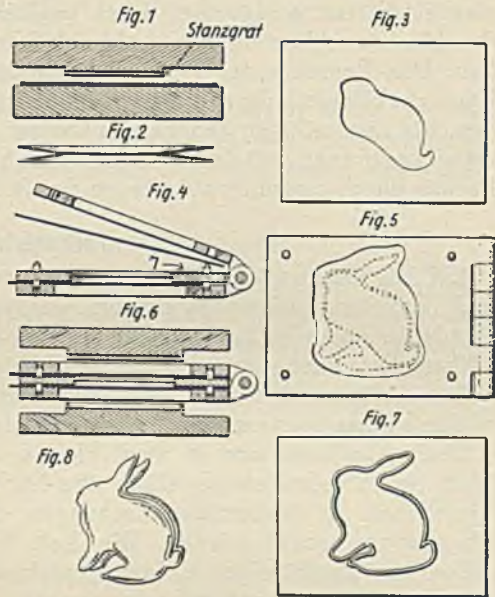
Stanzwerkzeug für Hohlkörper aus vier Blättern nach Stein
